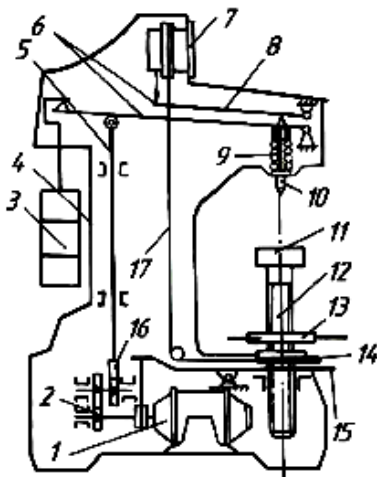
Прилад для вимірювання твердості за Роквеллом типу ТК-2М: 1 – електродвигун; 2 – черв'ячний редуктор; 3 – вантажі; 4 – корпус приладу; 5 – шток; 6 – підвіска; 7 – індикатор; 8 – важіль; 9 – пружина; 10 – наконечник з індентором; 11 – підйомний столик; 12, 13 – пара гвинт – маховик; 14 – механізм підйомного столика; 15 – педаль; 16 - кулачковий блок; 17 – трос
